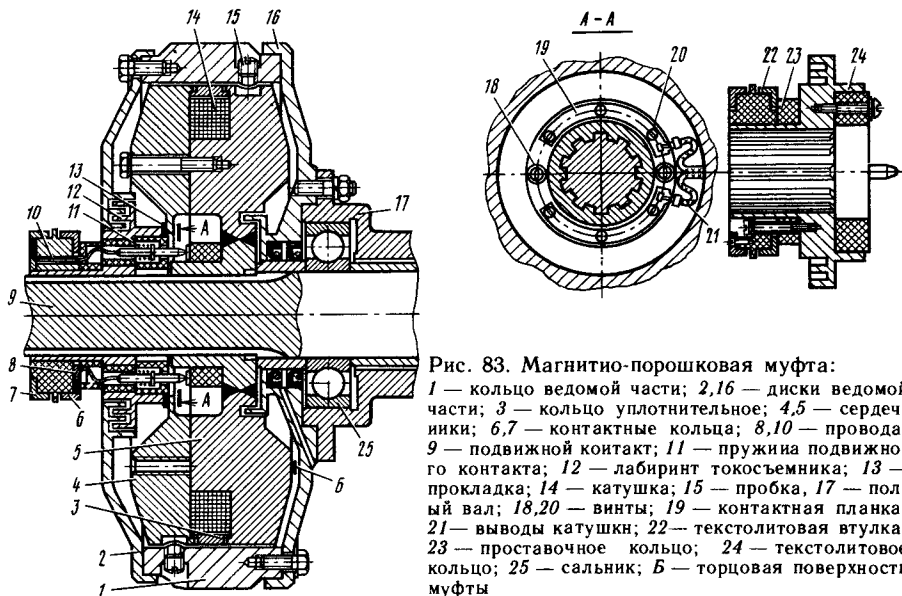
Магнитно-порошковая муфта: 1 — кольцо ведомой части; 2, 16 — диски ведомой части; 3 — кольцо уплотнительное; 4, 5 — сердечники; 6, 7 — контактные кольца; 8, 10 — провода; 9 — подвижной контакт; 11 — пружина подвижного контакта; 12 — лабиринт токосъемника; 13 — прокладка; 14 — катушка; 15 — пробка; 17 — полый вал; 18, 20 — винты; 19 — контактная планка; 21 — выводы катушки; 22 — текстолитовая втулка; 23 — проставочное кольцо; 24 — текстолитовое кольцо; 25 — сальник; Б — торцовая поверхность муфты
